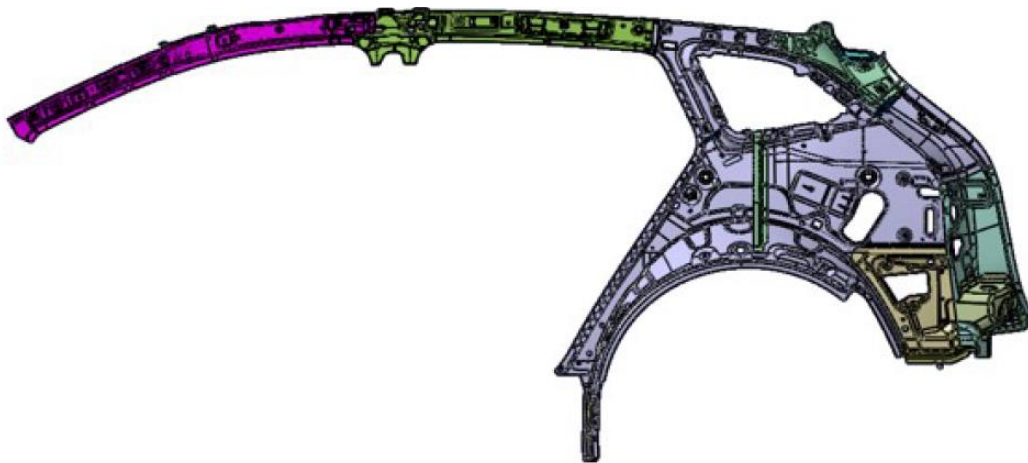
Bodový plán robotického odporového svařování ve stanici 3280 (R01) [13]
